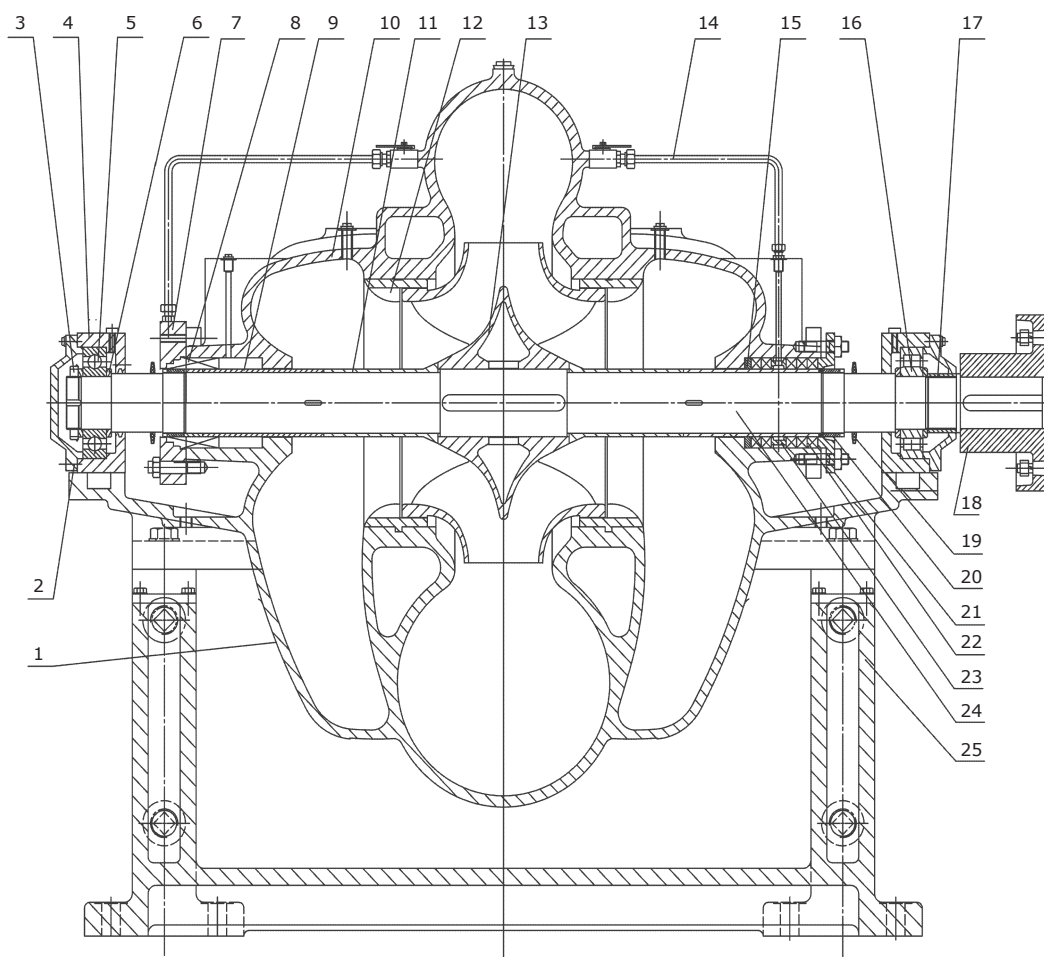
Вид в разрезе, стандартный тип исполнения 3
